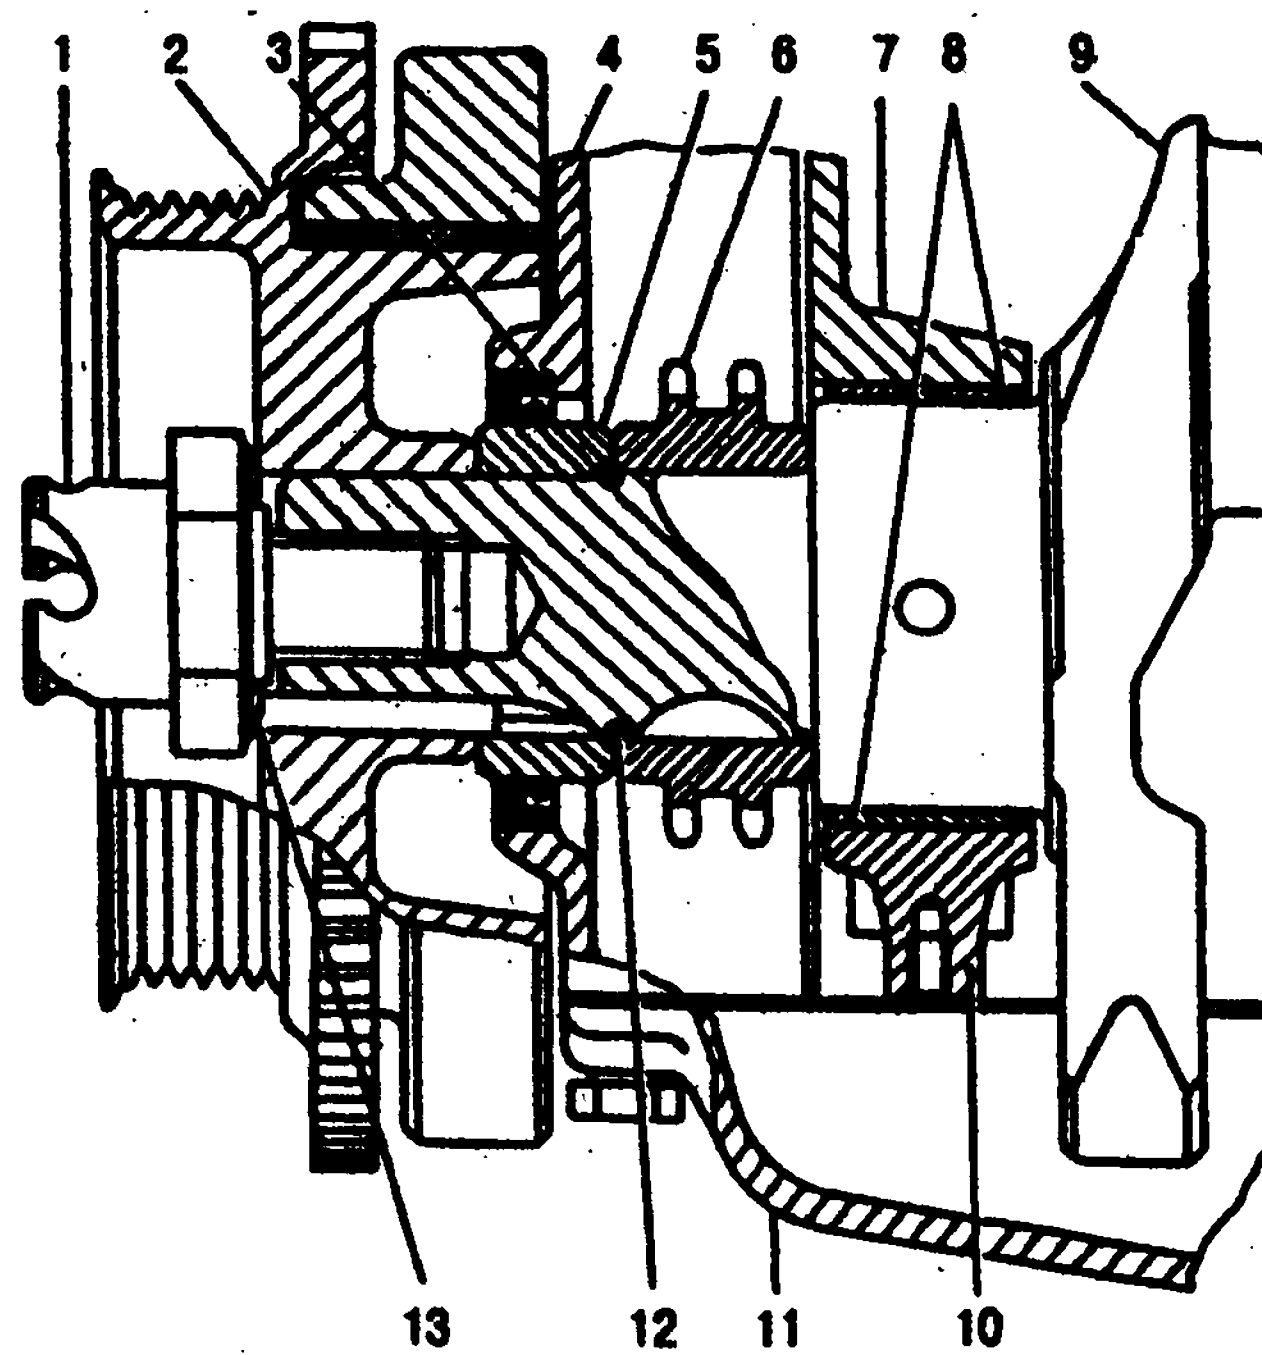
Передний конец коленчатого вала: 1 - храповик (или болт); 2 - шкив-демпфер с диском синхронизации; 3 - манжета; 4 - крышка цепи; 5 - втулка; 6 - звездочка; 7 - блок цилиндров; 8 - вкладыши подшипника, 9 - коленчатый вал; 10 - крышка подшипника; 11 - масляный картер; 12 - резиновое уплотнительное кольцо; 13 - стопорная шайба храповика
